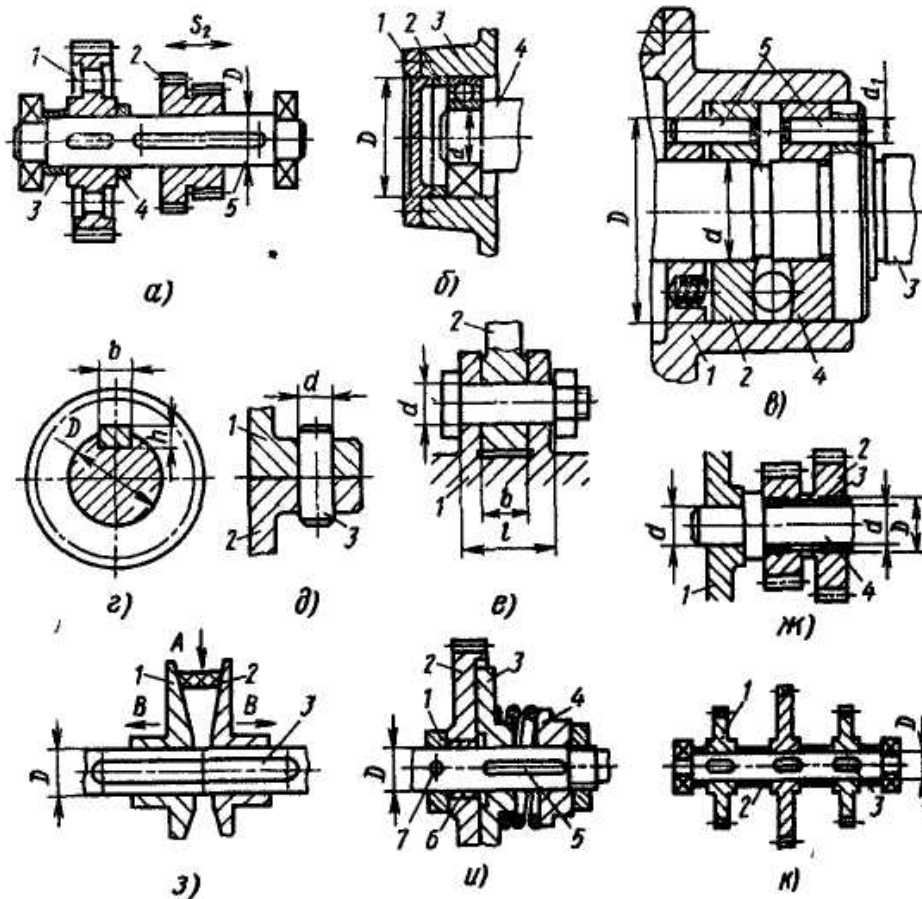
Ескізи з'єднань до питання 2.29.
